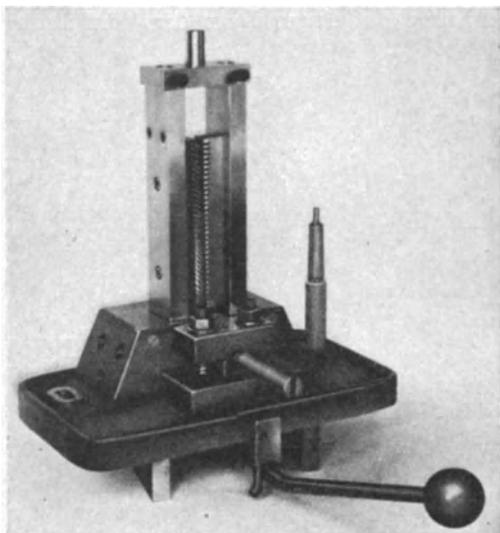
Außenräumvorrichtung mit parallel geführter Spannbacke, die durch ein unter dem Tisch befindliches Exzenter angezogen wird (Schilling).
